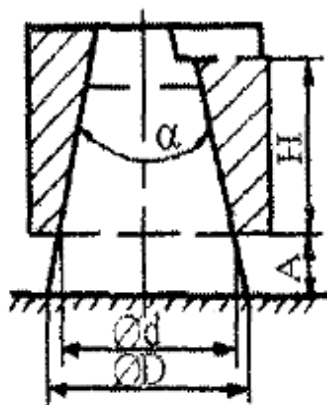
Схема встановлення заготовки на конічний отвір
